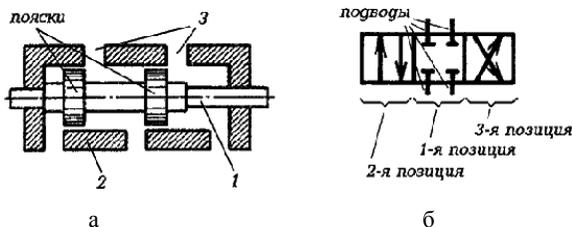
Схема (а) и обозначение (б) гидрораспределителя
